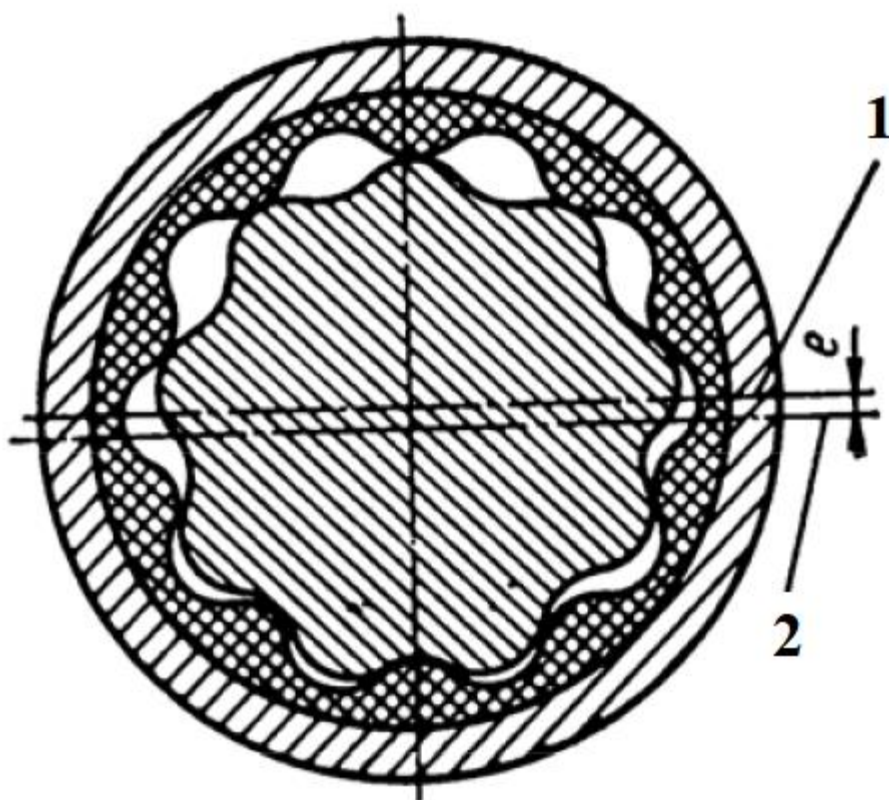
Поперечний переріз багатозахідних робочих органів
